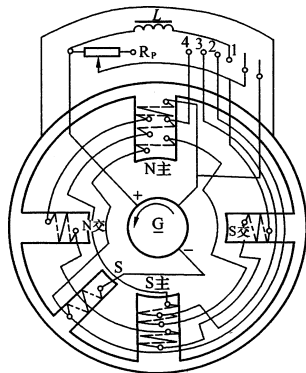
AX1-165 型直流弧焊机电气线路
